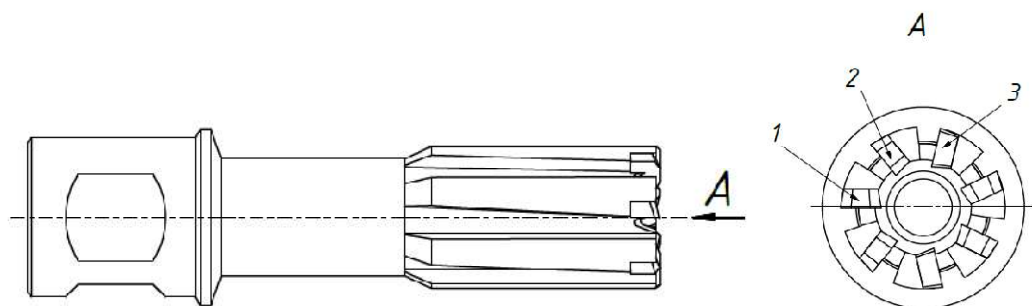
Рейкове корончатє свердло фірми Karnasch
